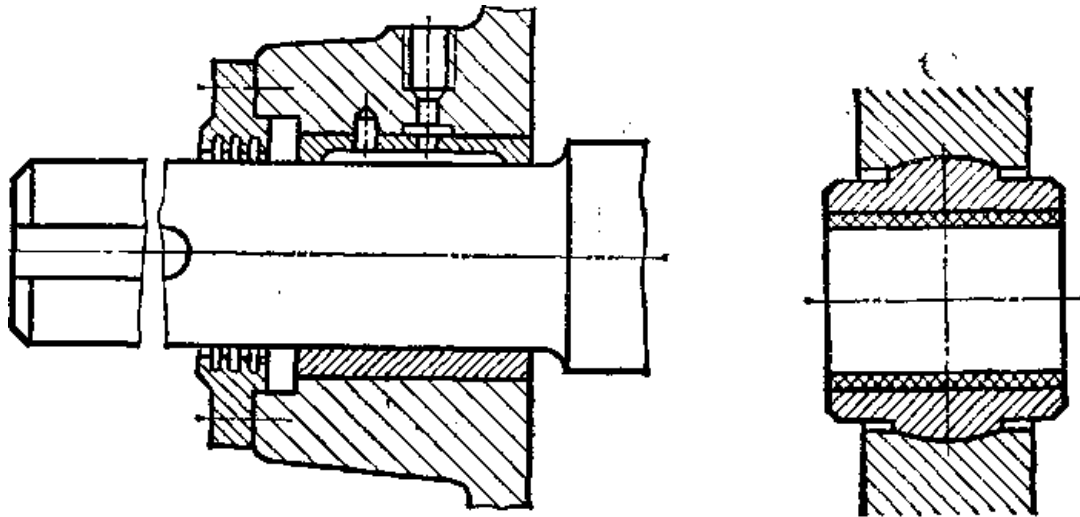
Конструкція підшипника, що самовстановлюється
